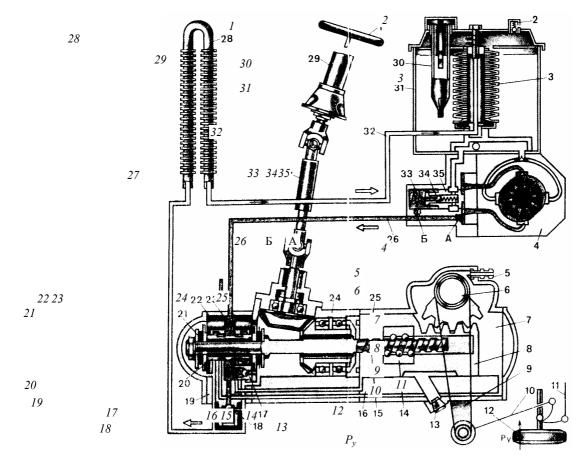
Схема гадроусилителя рулевого механизма автомобилей КамАЗ: 1 – рулевое колесо; 2, 18, 34 – предохранительные клапаны; 3 – сливной фильтр; 4 – насос; 5, 35 – перепускные клапаны; 6 – вал сошки с зубчатым сектором; 7 – задняя полость гидроусилителя; 8 – поршень-рейка; 9 – сошка; 10 – продольная тяга; 11 – поперечная тяга; 12 – переднее колесо; 13 – магнитная сливная пробка; 14 – шариковая гайка; 15 – винт; 16 – корпус рулевого механизма; 17 – обратный клапан; 19 – корпус распределителя; 20 – золотник; 21 – упорный подшипник; 22 – реактивный плунжер; 23 – центрирующая пружина; 24 – корпус углового редуктора; 25 – передняя полость гидроусилителя; 26 – напорная гидролиния; 27 – карданный вал; 28 – радиатор; 29 – рулевая колонка; 30 – заливной фильтр; 31 – бачок; 32 – гидролиния слива; 33 – пружина перепускного клапана насоса; А и Б – дросселирующие отверстия
